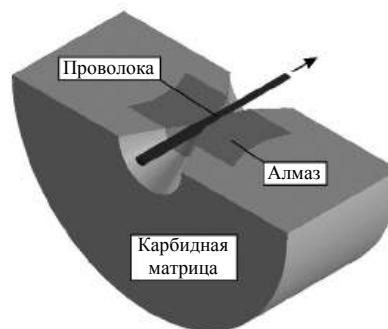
Геометрическая модель волоки и движущейся заготовки в разрезе
